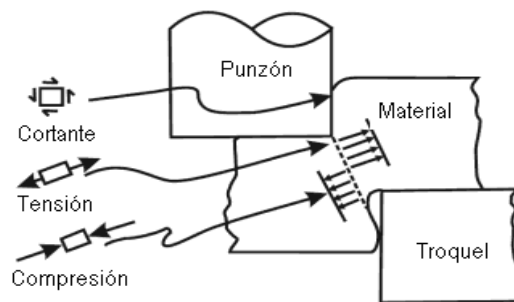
Fuerzas Cortante, de tensión y compresión durante el troquelado
